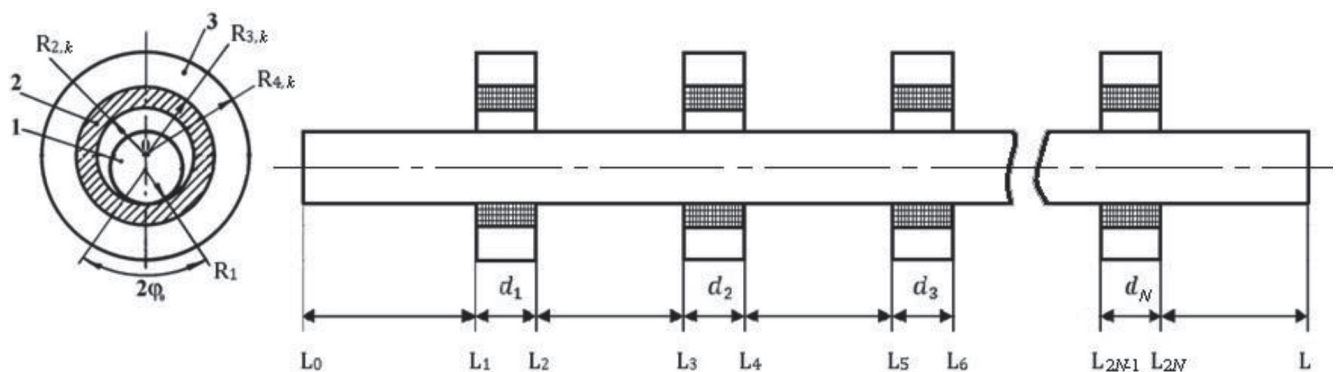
Модель системы подшипников скольжения: 1 – вал; 2 – втулка; 3 – корпус
